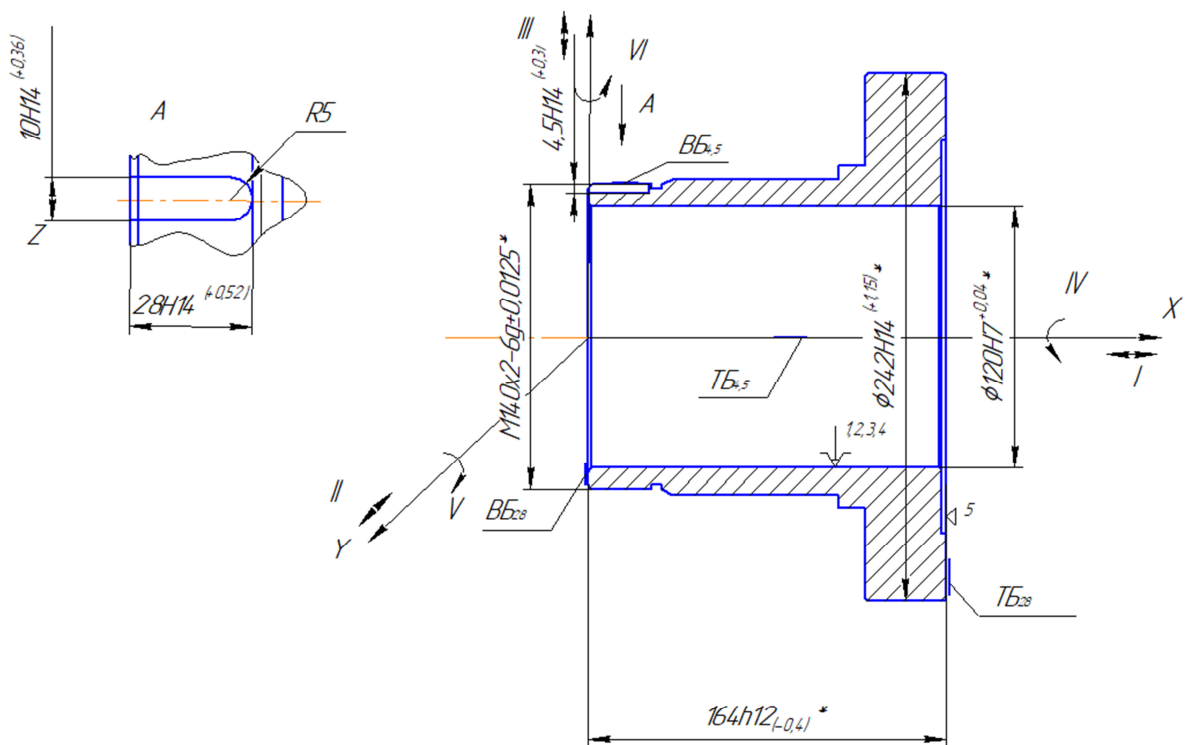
Схема базування заготовки (Позиція I).
